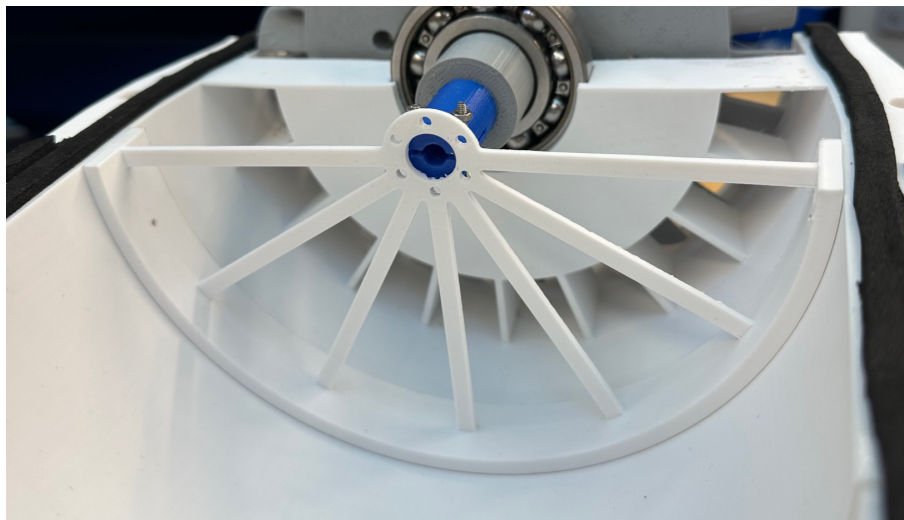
Axel monterad med modifierad turbindel utan blad för test av endast kompressor.
